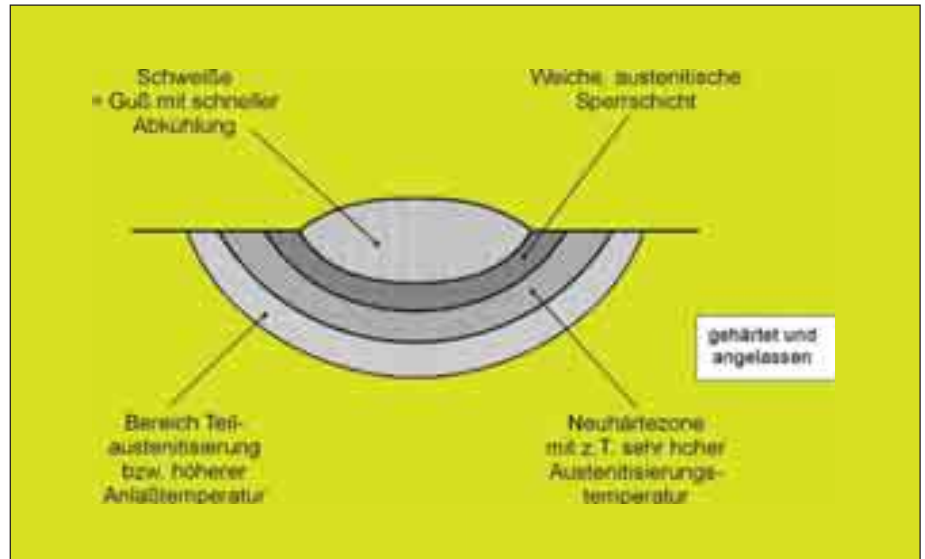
Härteausbildung im Schweißnahtumfeld bei gehärtetem und angelassenem Stahlguss
